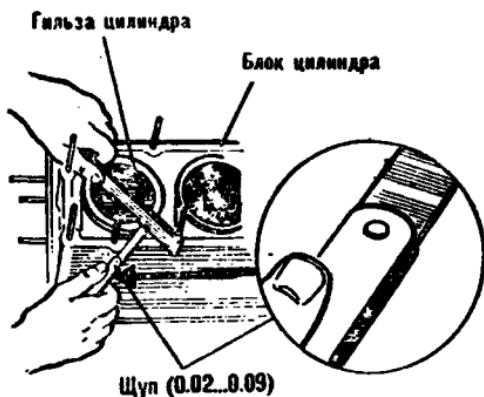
Установка гильз в блоке цилиндров двигателя ЗМЗ-53-12
